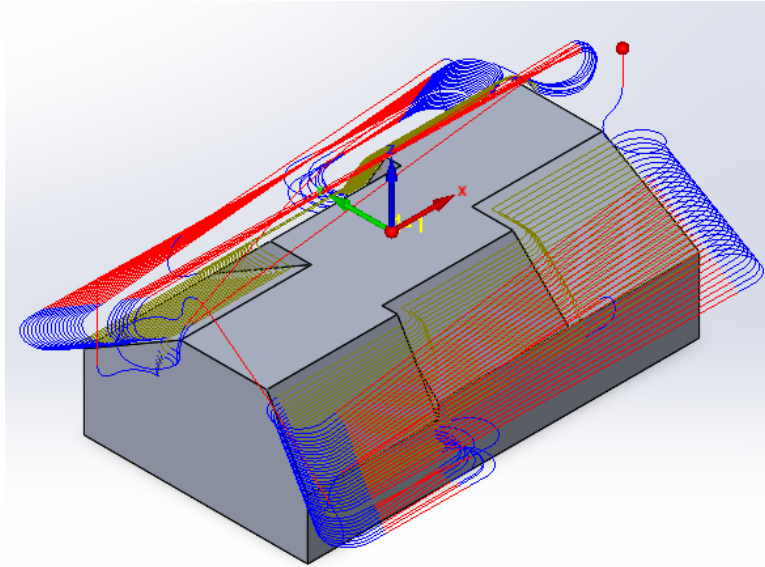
Trajetória executada durante a operação de maquinação de Z constante
